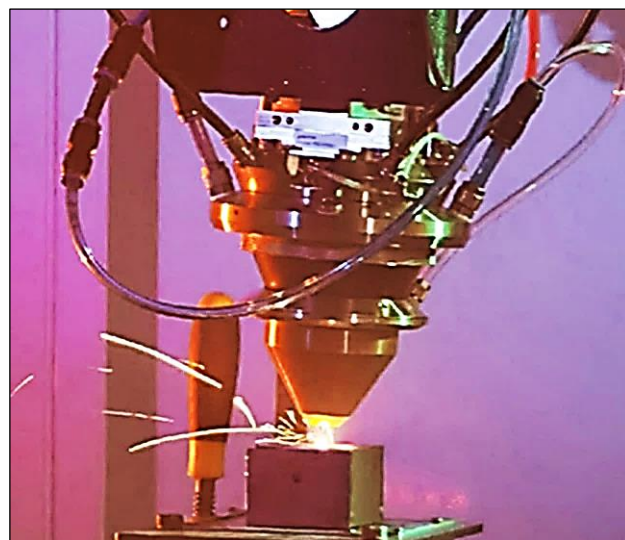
Фотография процесса лазерного выращивания металломатричного композита.
